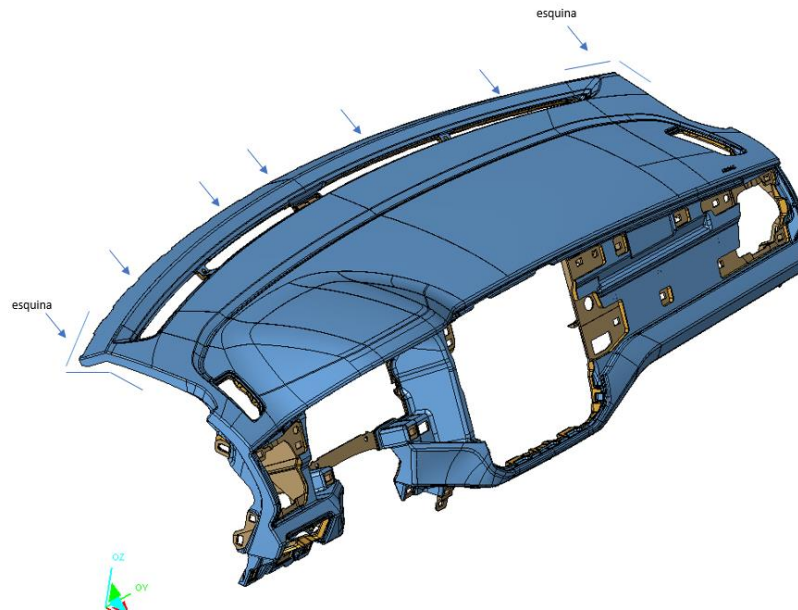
Salpicadero con zonas donde colocar apoyos
